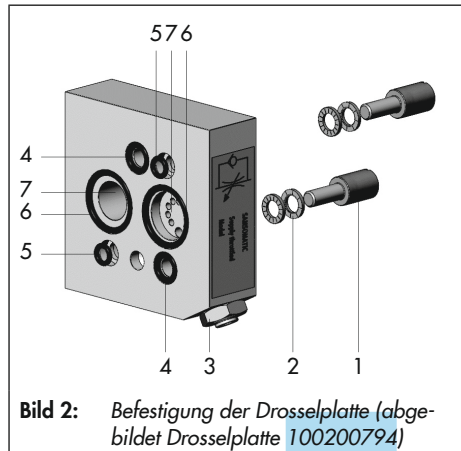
Befestigung der Drosselplatte (abgebildet Drosselplatte 100200794)
